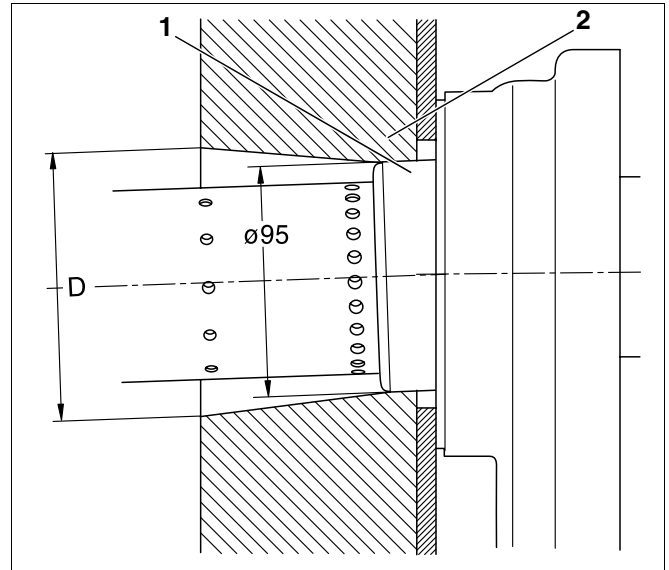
Coupe sur la porte brûleur (dimension en mm)
